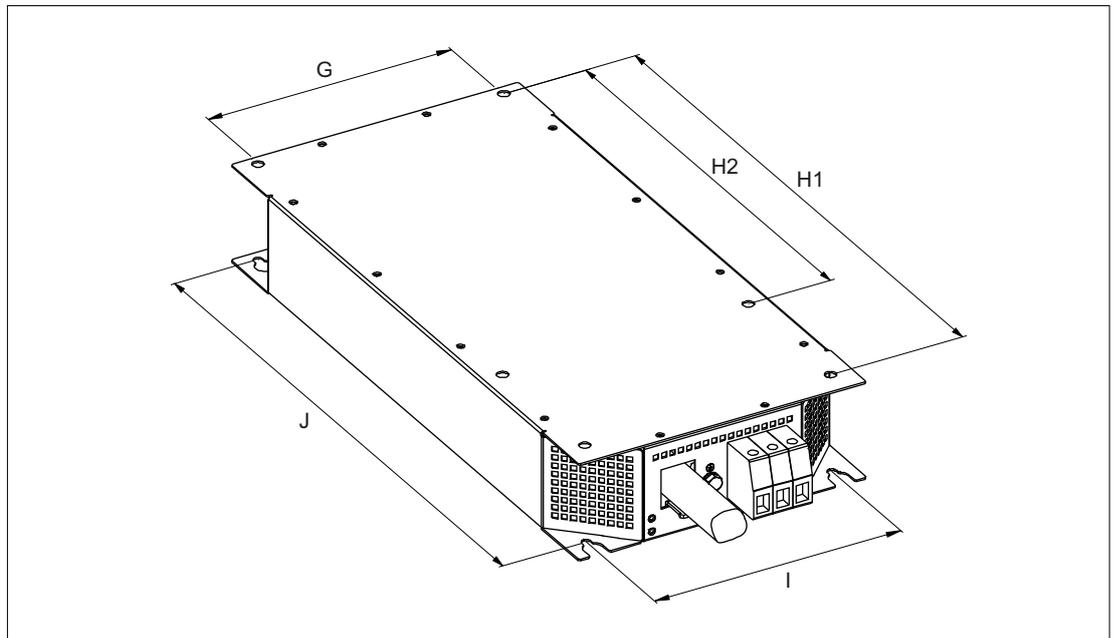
Quote di montaggio della bobina di rete, grandezze costruttive FSD e FSE
